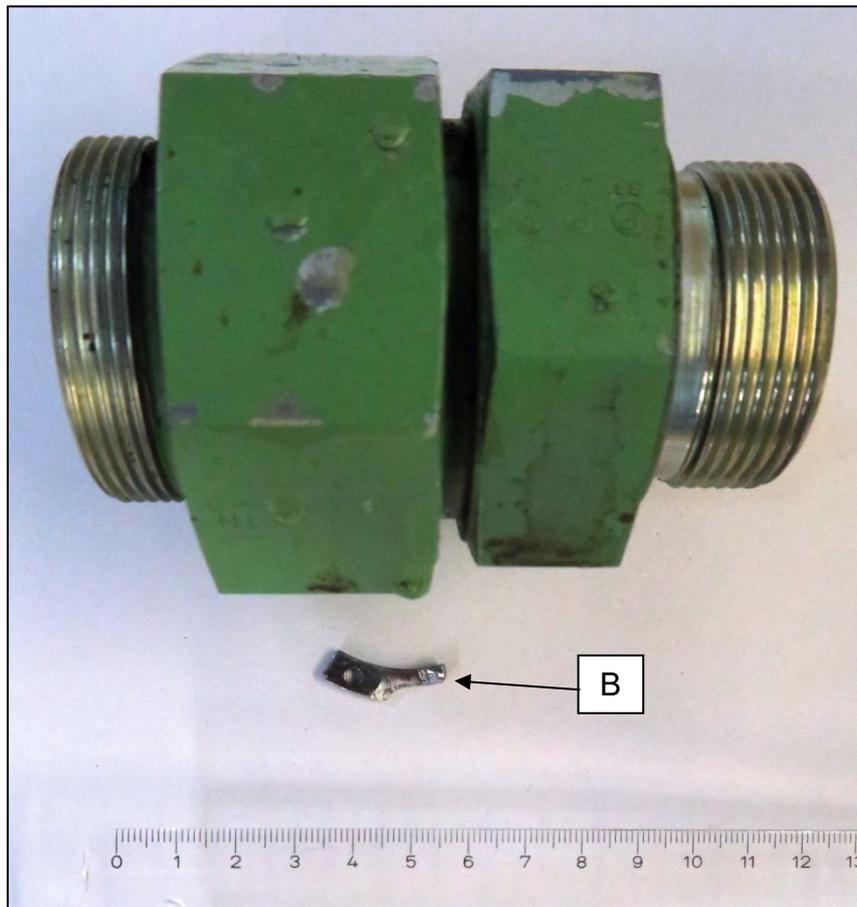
Rückschlagventil und entfernter Fremdkörper
